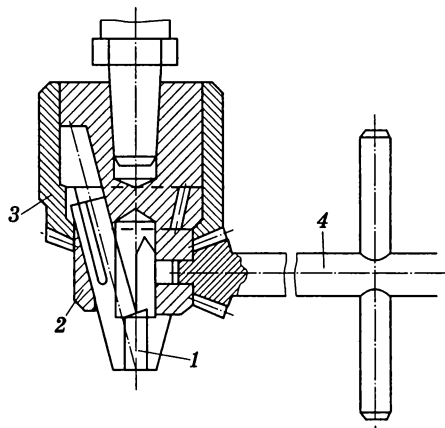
Устройство и принцип работы трехкулачкового патрона с наклонными кулачками:
